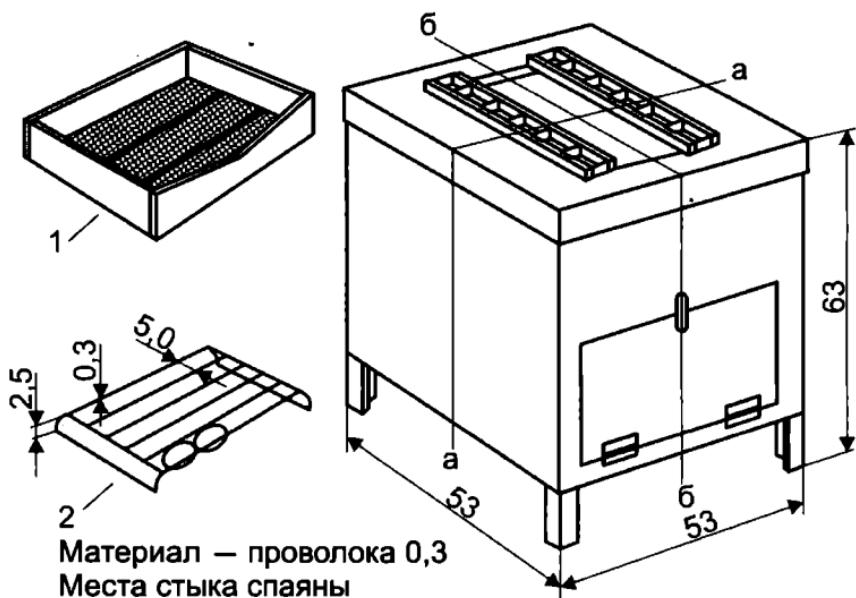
Инкубатор конструкции Н. П. Третьякова:
